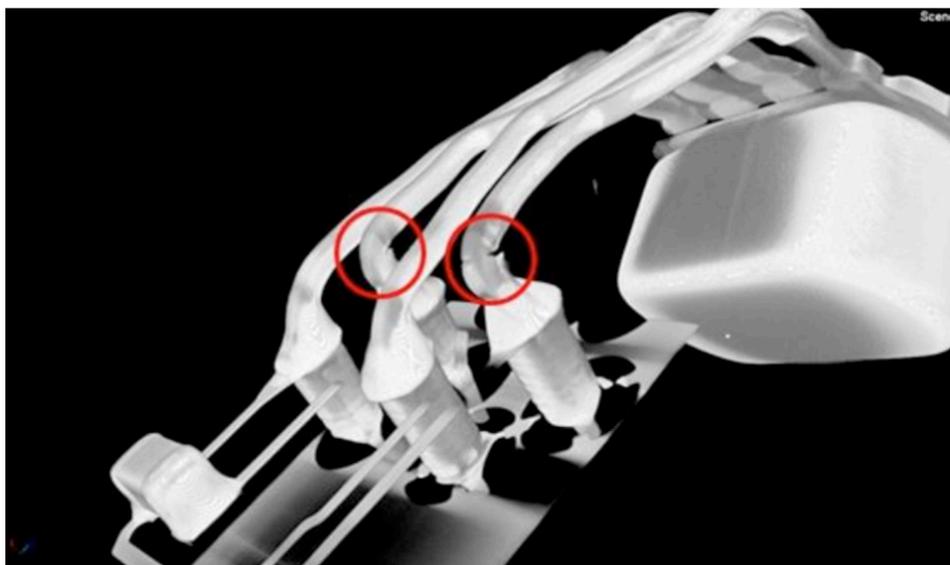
Imagen en “3D” del sensor magnético soldado en las cuatro terminales, que muestran fracturas indicados en los círculos rojos de 2 de sus terminales. Las partes brillantes son las partes metálicas del sensor magnético de transmisión automática automotriz.
